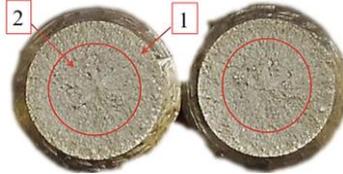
Образец стали класса прочности K56 после испытаний
